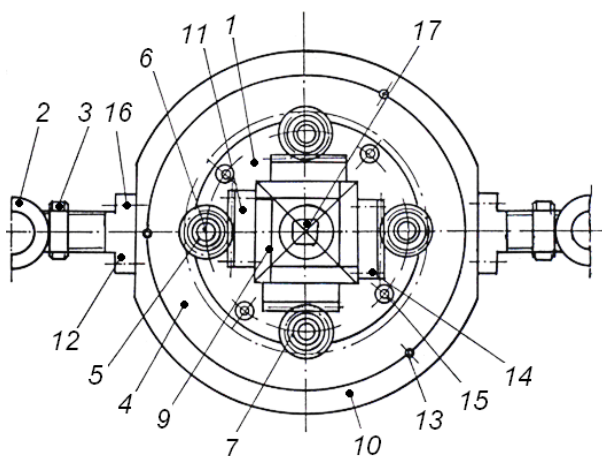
Схема лабораторного устройства горячей четырехножевой резки прутковых заготовок: 1 – корпус устройства; 2 – скобка-втулка; 3 – гайка; 4 – солнечное зубчатое колесо; 5 – втулка; 6 – ось; 7 – шестерня-сателлит; 9 – нож; 10 – бандаж; 11 – рейка; 12 – упор; 13 – стопорный винт; 14 – болт; 15 – опорная втулка; 16 – болт; 17 – заготовка
